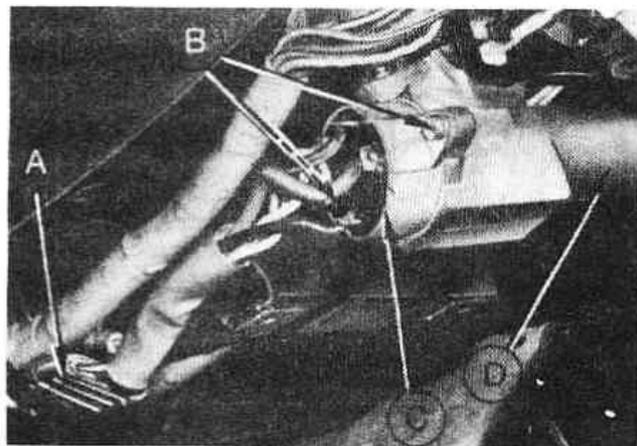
Разъедините разъем (A) и выверните два винта (B), чтобы отсоединить выключатель зажигания (C) от замка рулевой колонки (D) (Разд.42)
